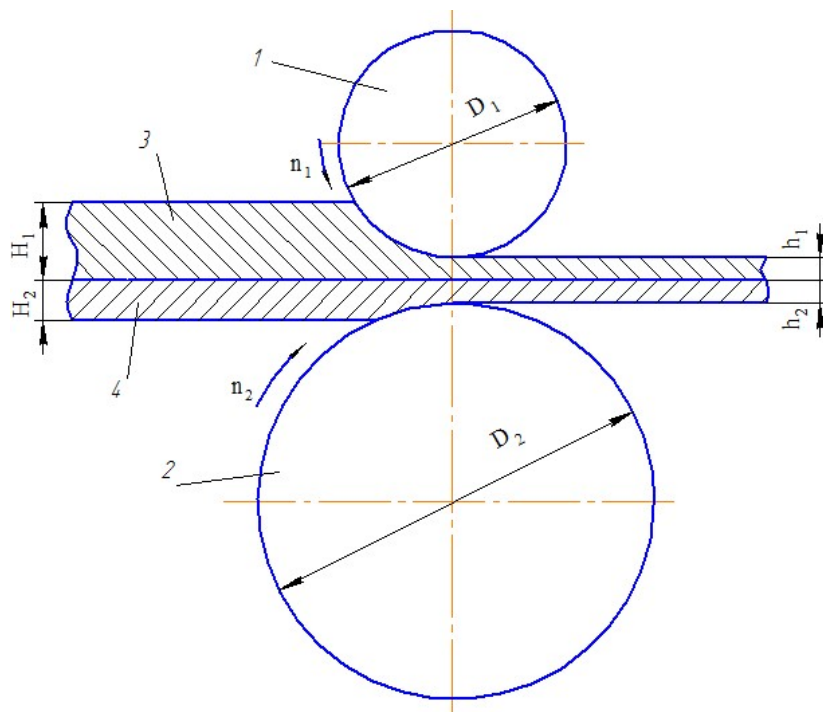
Отримання біметалів прокаткою у валках різного діаметру: 1 і 2 - робочі валки; 3 та 4 – шари композиції
